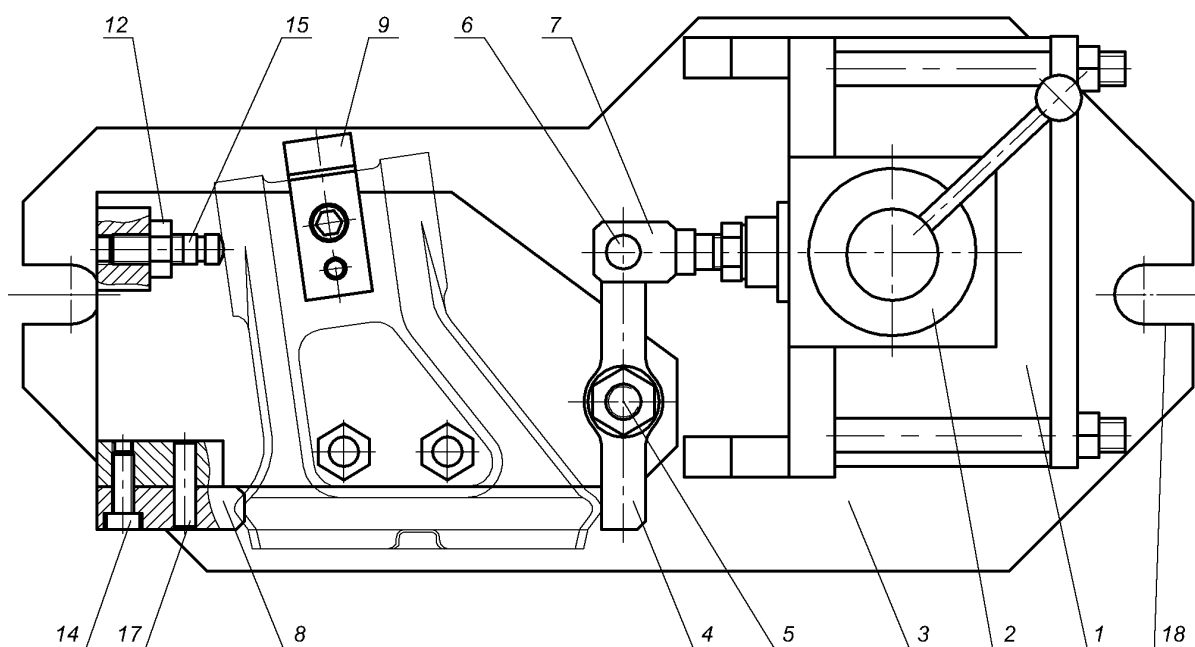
Пристрій для фрезерування торця в деталі 54-62136Б
